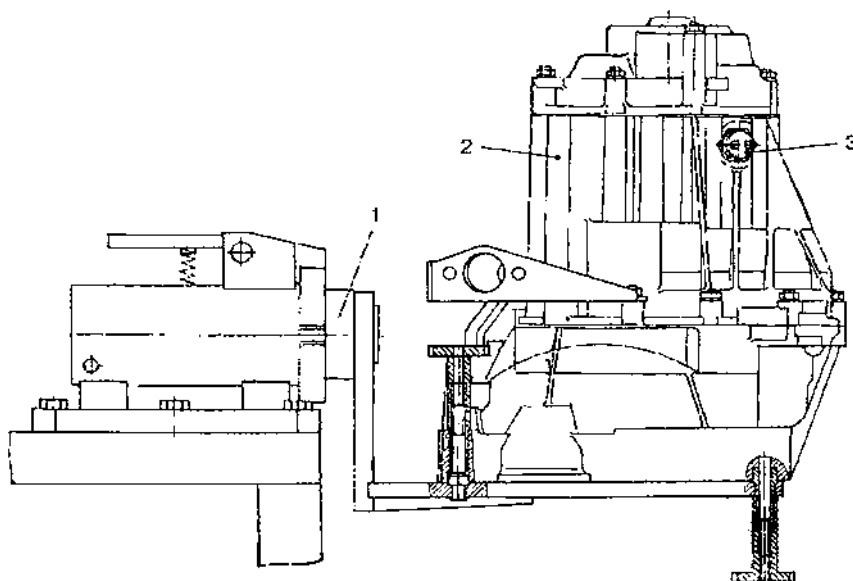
Коробка передач, установленная на приспособлении для разборки и сборки:
